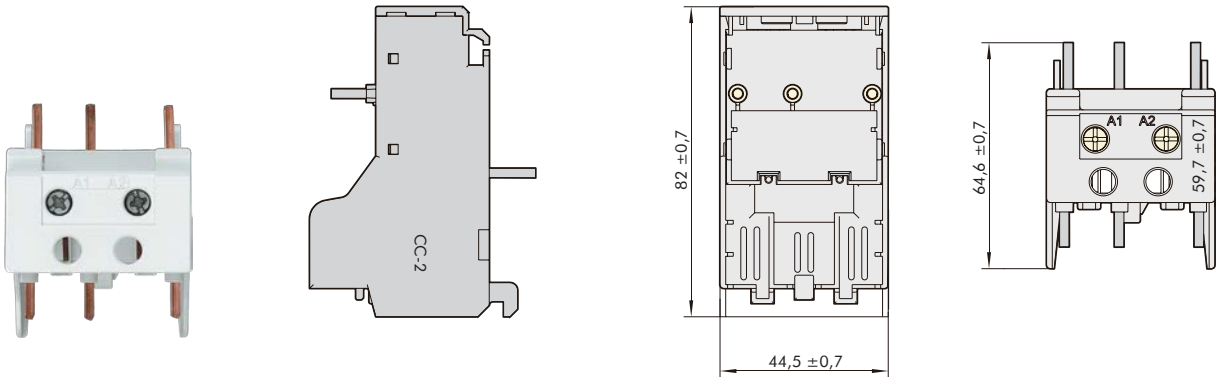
Vue d'ensemble et dimensions d'installation du CC-3(NS2)
